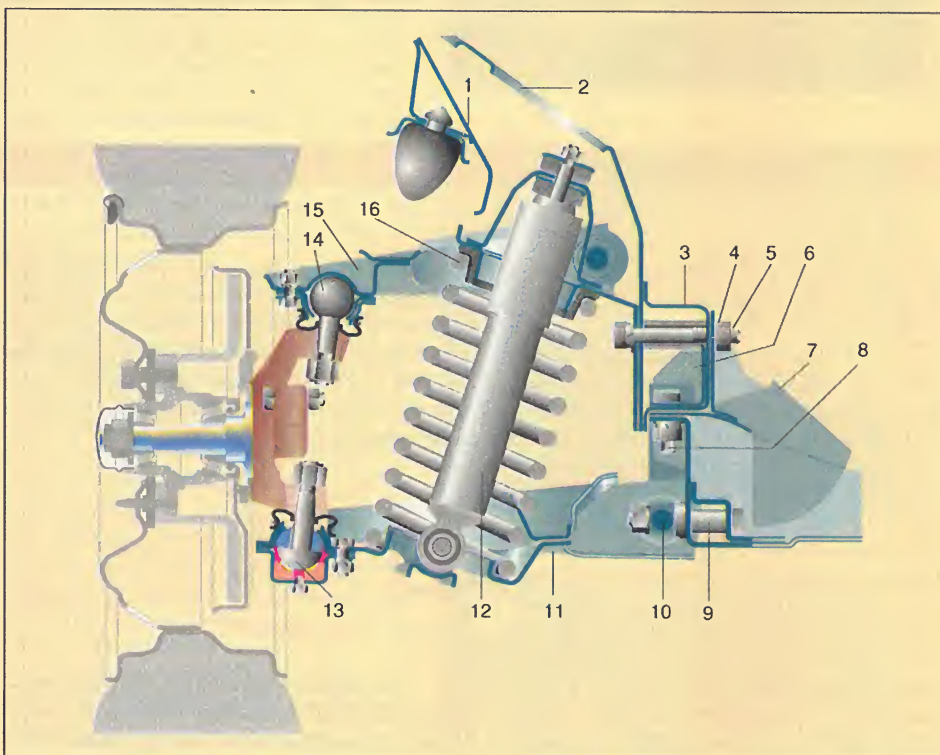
Схема передней подвески "Жигулей": 1 – стойка передка; 2 – брызговик; 3 – лонжерон; 4 – гайка; 5 – верхний горизонтальный болт; 6 – усилитель лонжерона; 7 – поперечина подвески; 8 – нижний вертикальный болт; 9 – болт крепления оси нижнего рычага; 10 – ось нижнего рычага; 11 – нижний рычаг; 12 – амортизатор; 13 – нижняя шаровая опора; 14 – верхняя шаровая опора; 15 – верхний рычаг; 16 – пружина.
